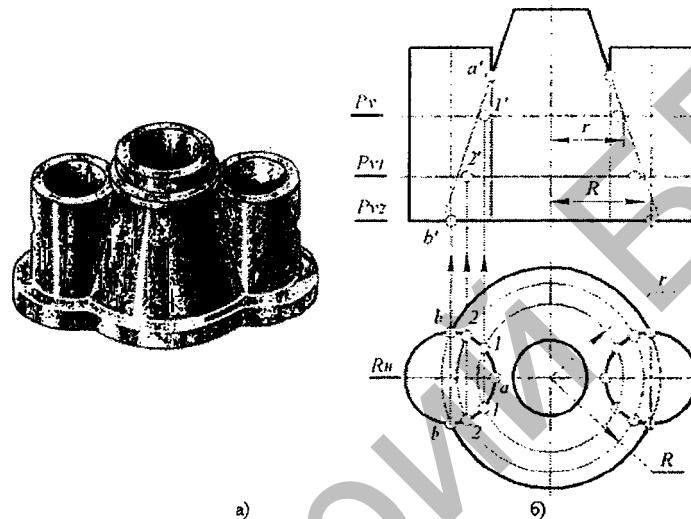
Пересечение конической и цилиндрических поверхностей:
